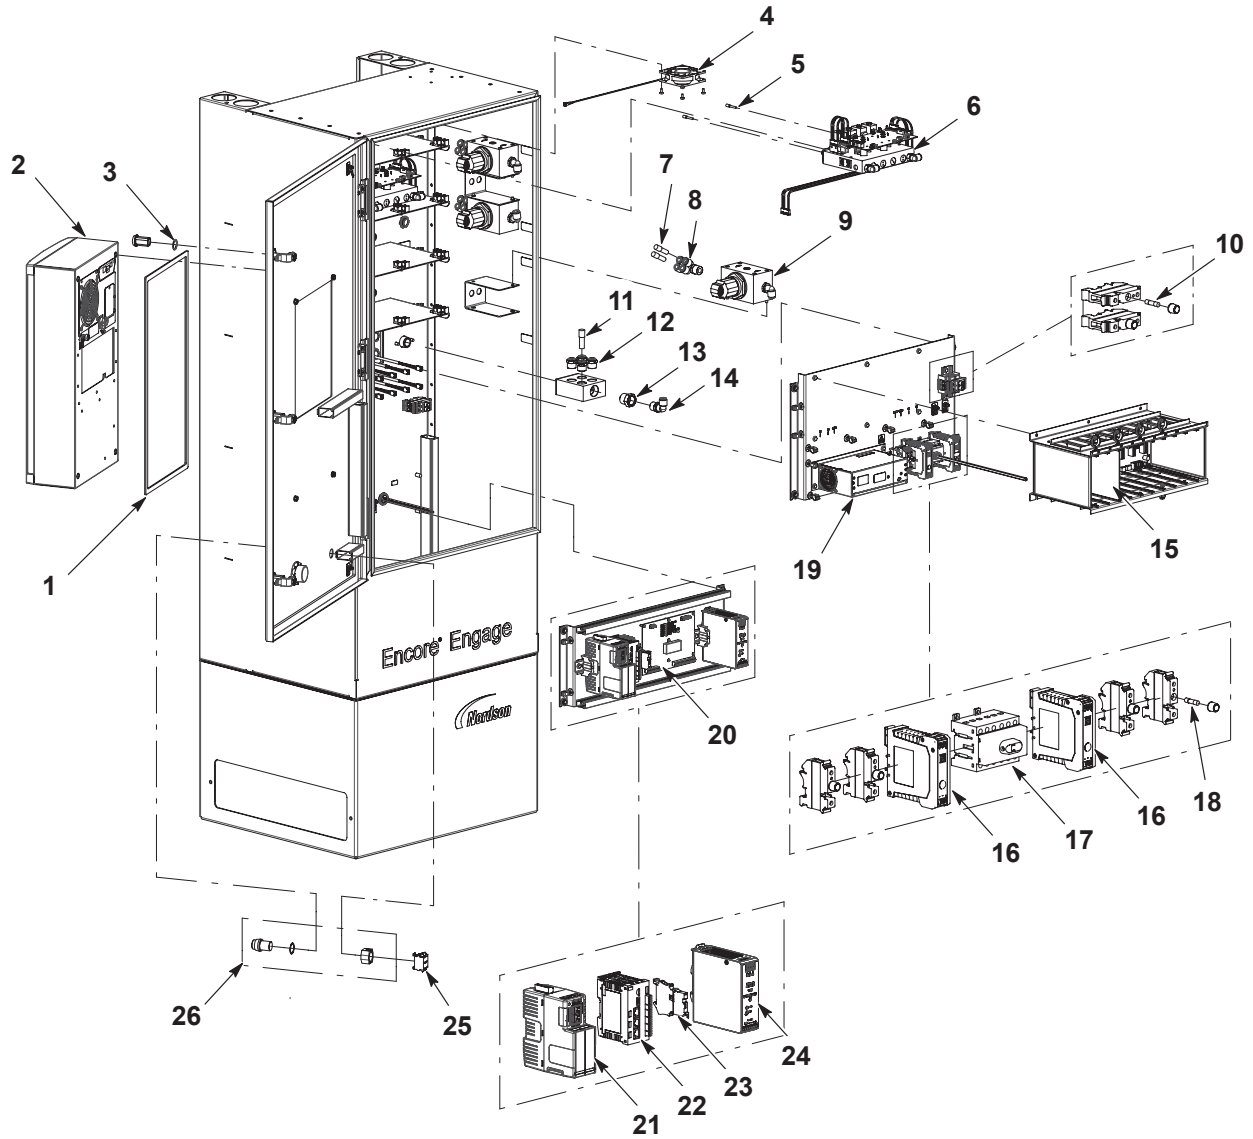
Hauptsteuerung für Komponenten der externen Anzeige mit Kühlgerät, 1 von 2
